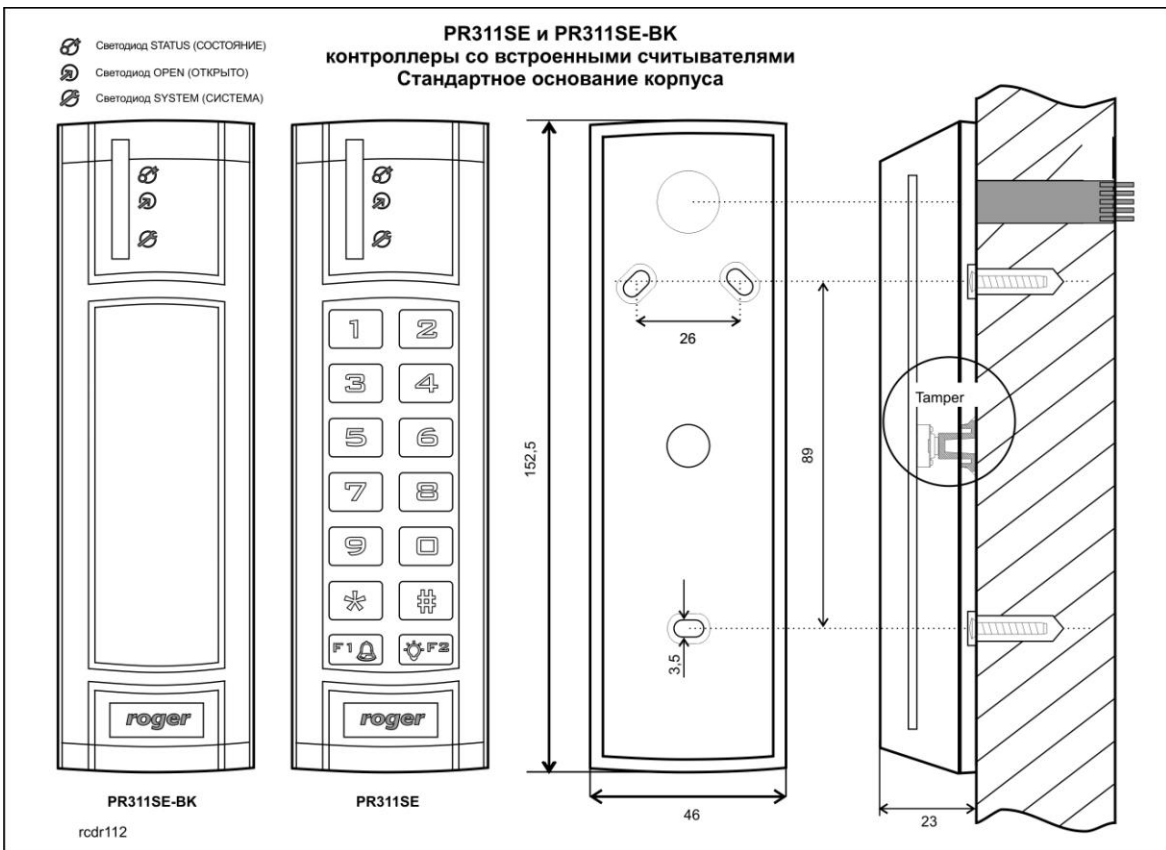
Контроллер PR311SE со стандартным основанием корпуса
